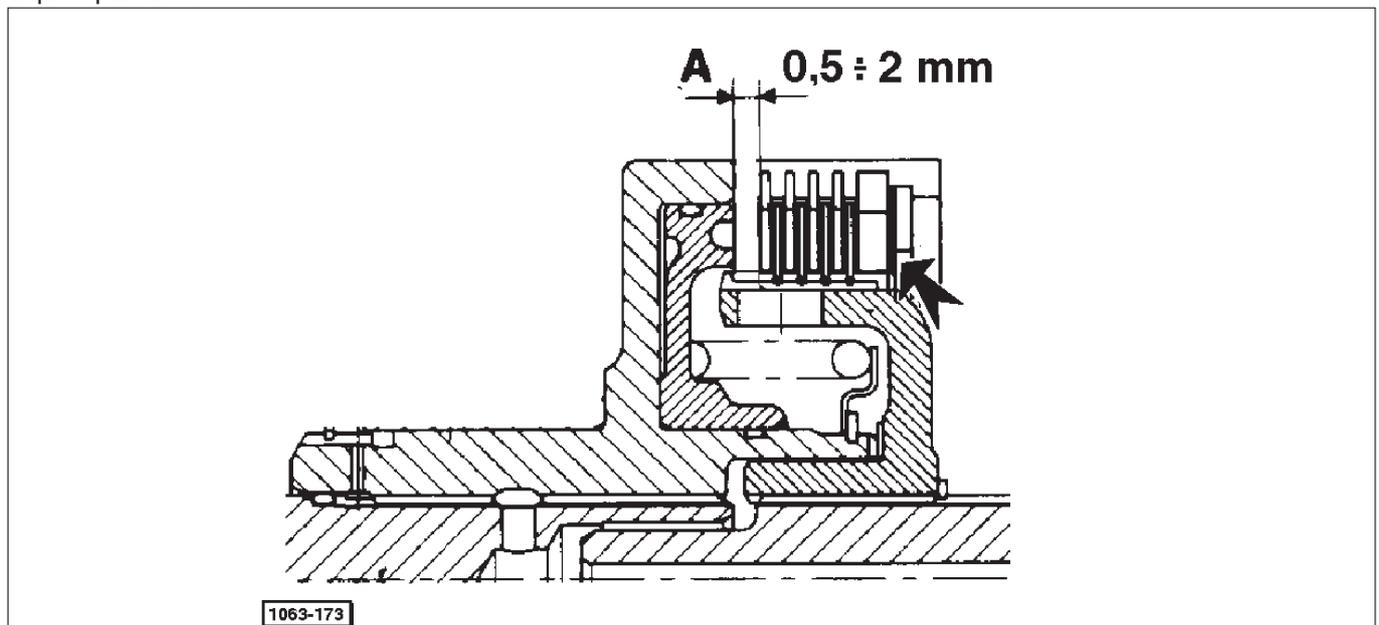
Contrôle du jeu des disques d'embrayage de la P.d.F. avant.
